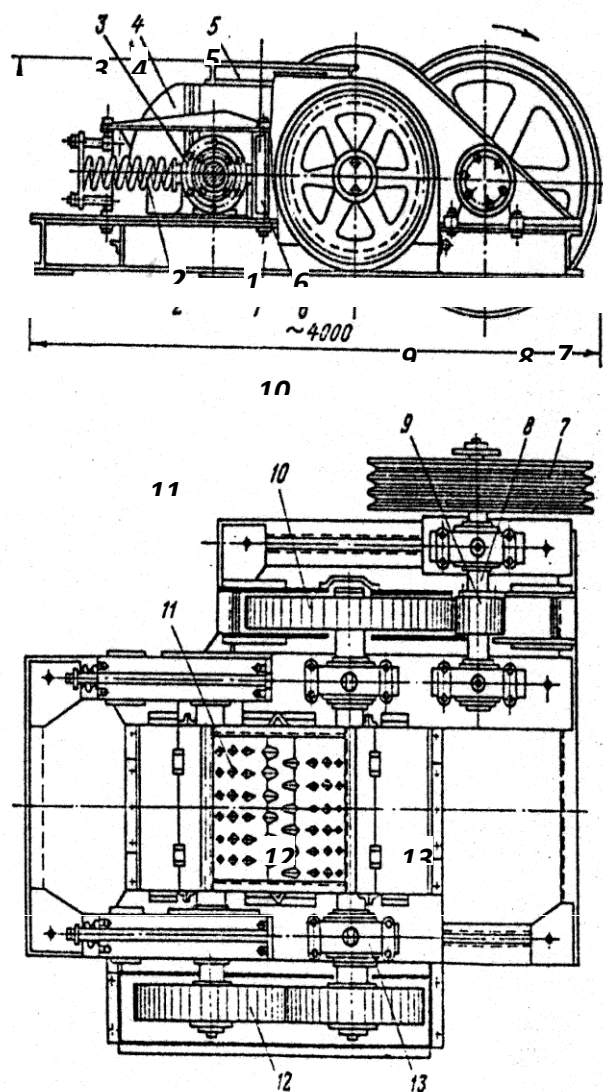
Двухвалковая зубчатая дробилка.
